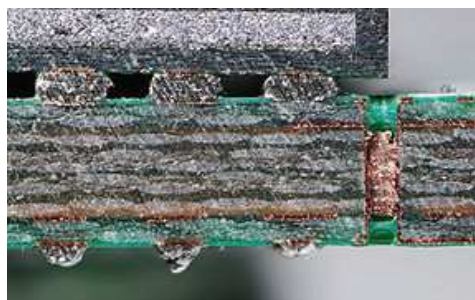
Circuit imprimé vu du côté soudures
